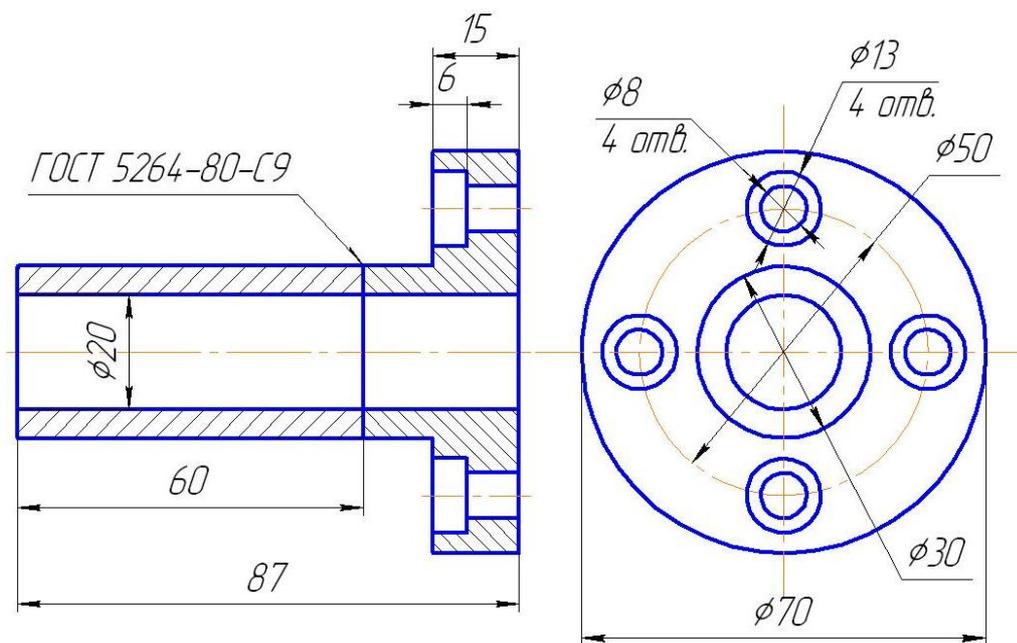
Стыковое сварное соединение, выполненное ручной дуговой сваркой
